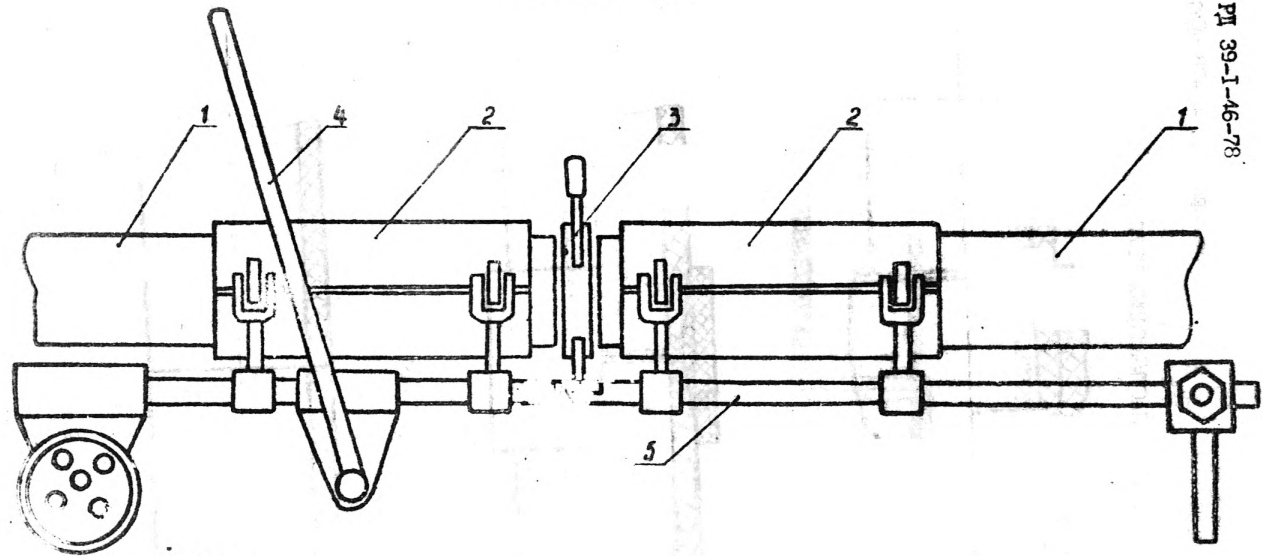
1 - труба полиэтиленовая; 2 - хомут зажимной; 3 - нагреватель;
